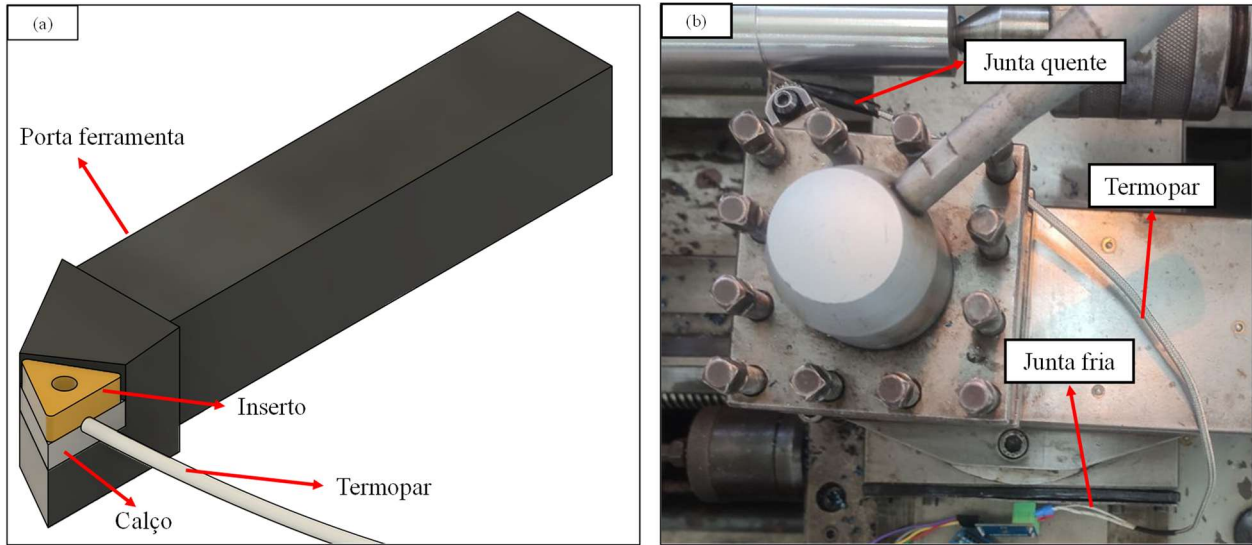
Junta quente do termopar fixado no porta ferramentas. (a) Desenho esquemático. (b) setup na máquina-ferramenta para ensaios de torneamento.
